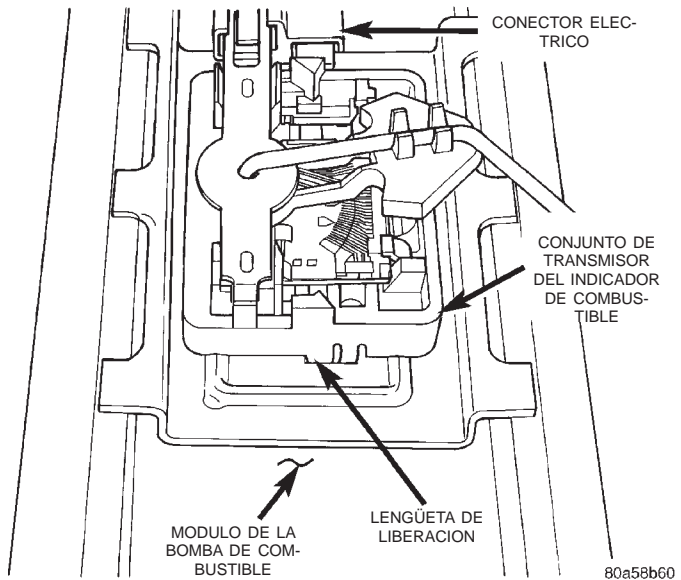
Lengüeta de liberación del conjunto de transmisor del indicador de combustible
